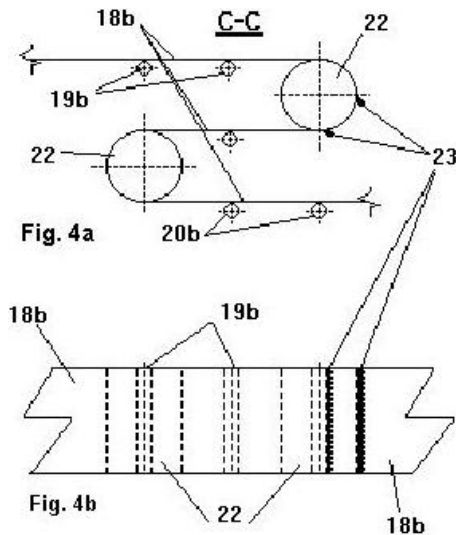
Puentes de viraje de los transportadores; a-Vista en la sección transversal desarrollada en el corte transversal en uno de los puentes de viraje; b-Vista en planta desarrollada sobre el corte transversal en uno de los puentes de viraje.
